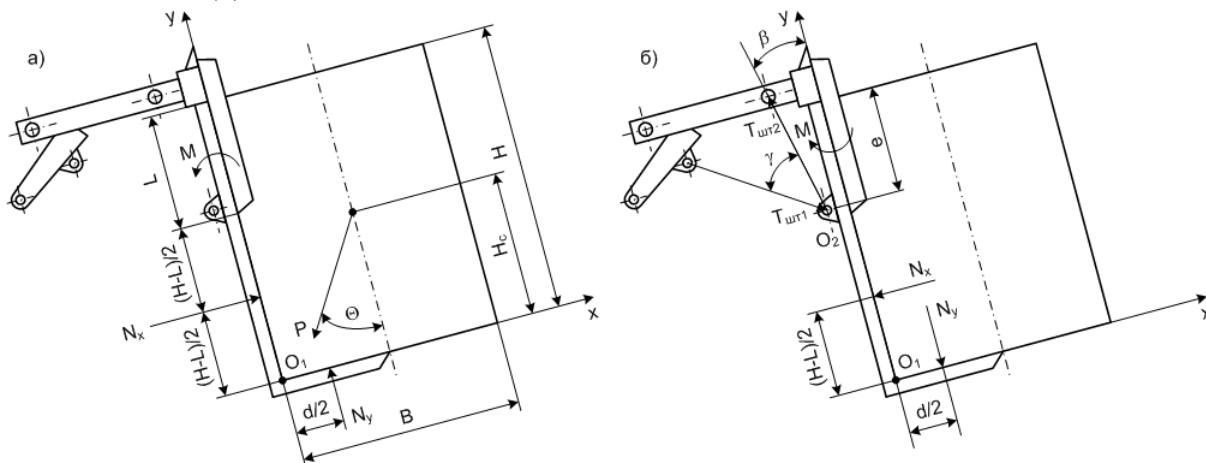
Расчетные схемы сил в системе «захват-бак-захват» для новой конструкции захвата:
